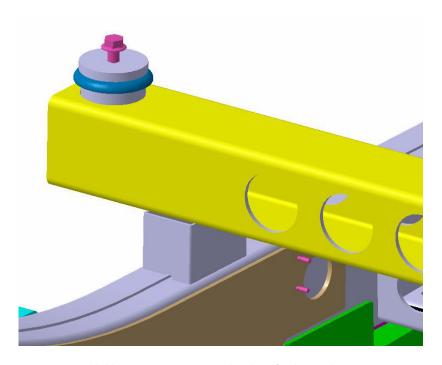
Querträgeres als Schweißteil am Rahmen
